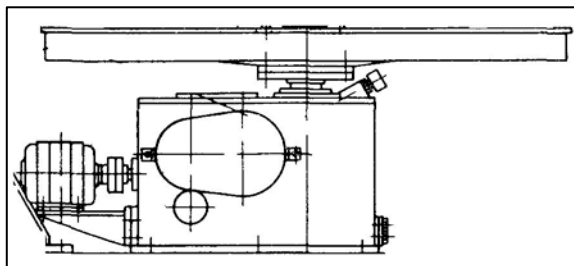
Общий вид поворотно-сварочного стола
